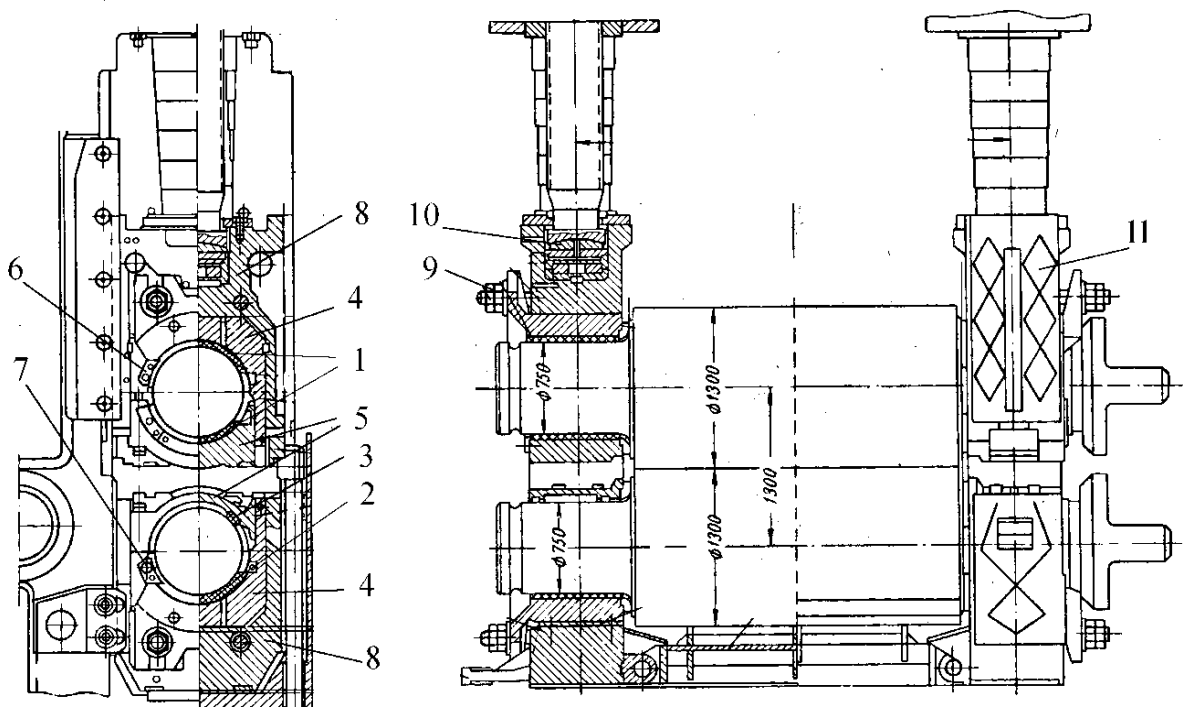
Валковий вузол обтискного стану на підшипниках ковзання
